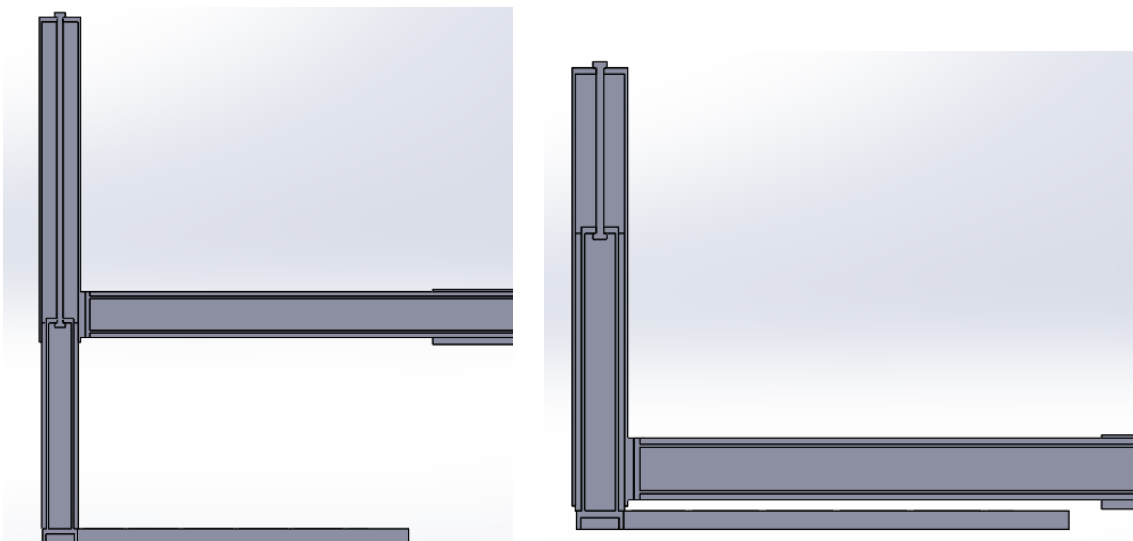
Condições do Modelo - Viga de Elevação Aberta e Fechada
